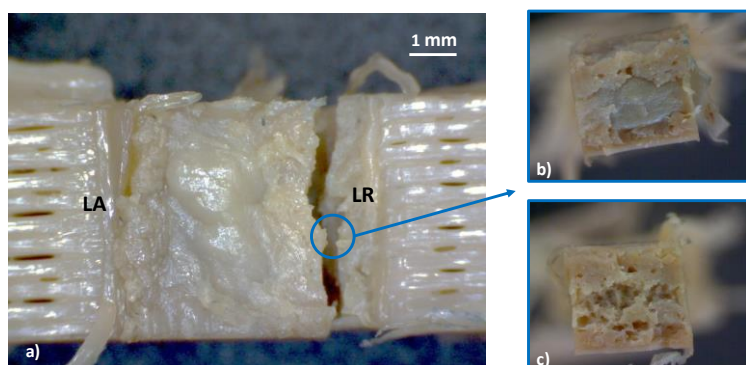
Macrografia do provete após Ensaio 4: a) Superfície superior do provete, b) Superfície de fratura do cordão de soldadura do LR, c) Superfície de fratura da interface do material base com o LR.
